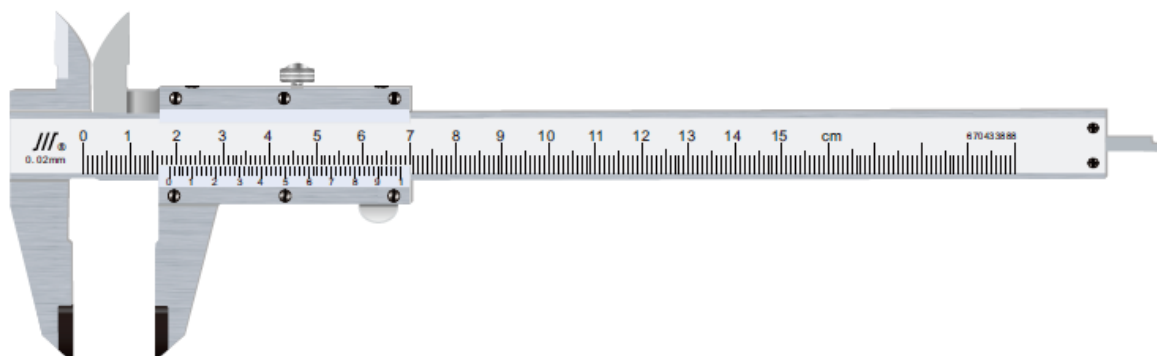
Общий вид штангенциркулей модели ШЦ-I
